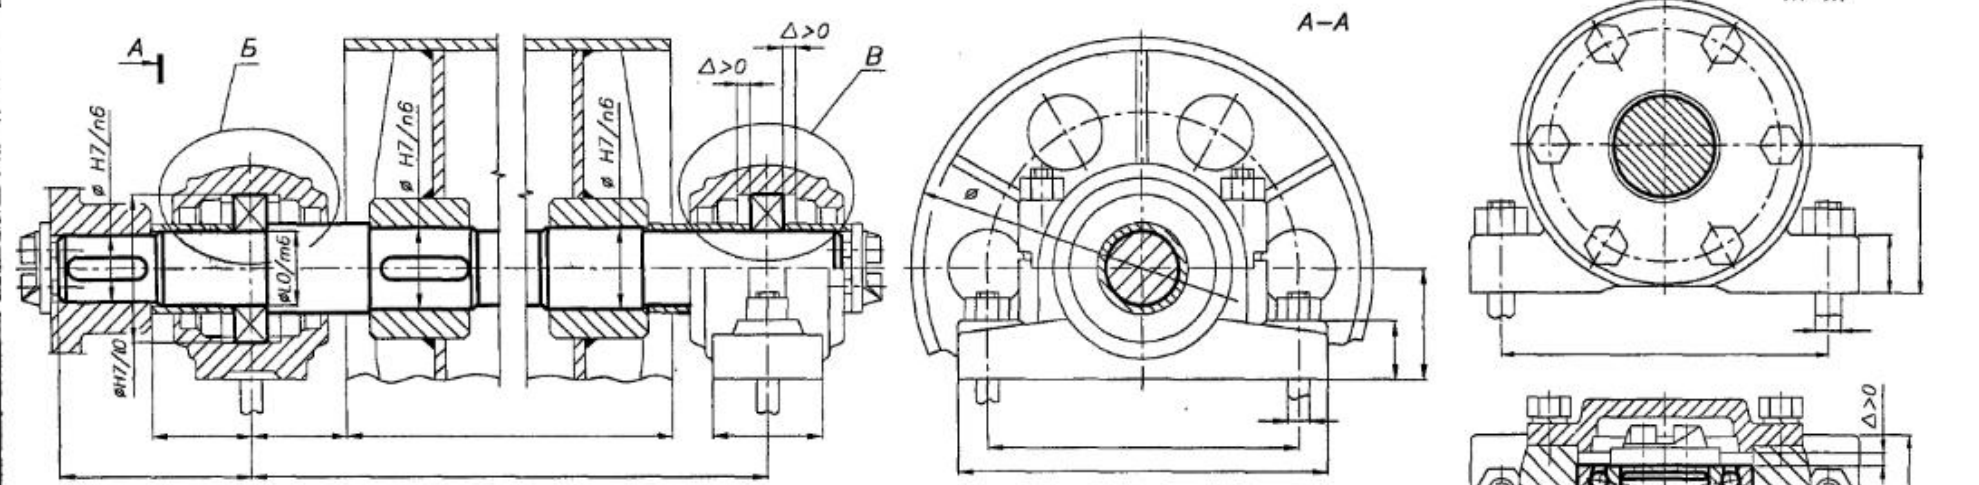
Подшипниковые узлы приводного вала барабана
